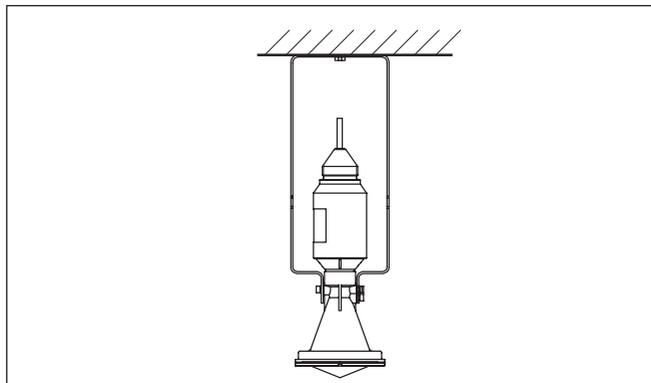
Вертикальный монтаж на перекрытии с помощью монтажной скобы длиной 300 мм
